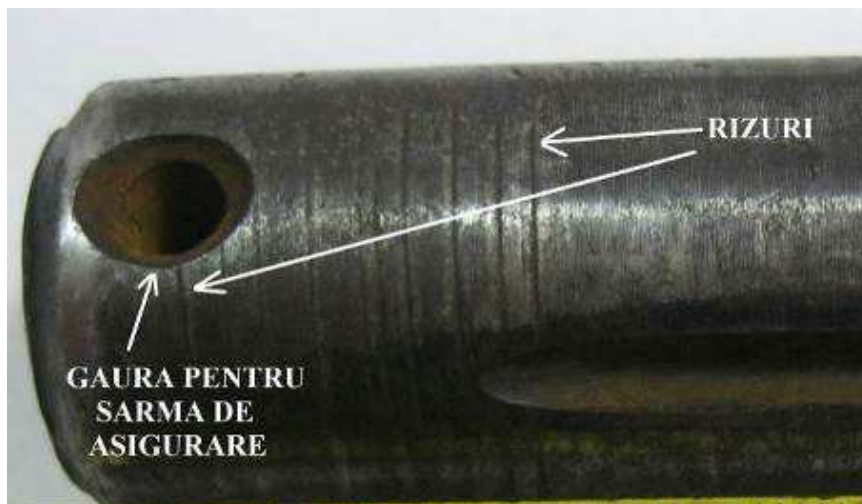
Detaliu rizuri pe suprafața de contact a bolțului cu falca inferioară a barei de tracțiune
